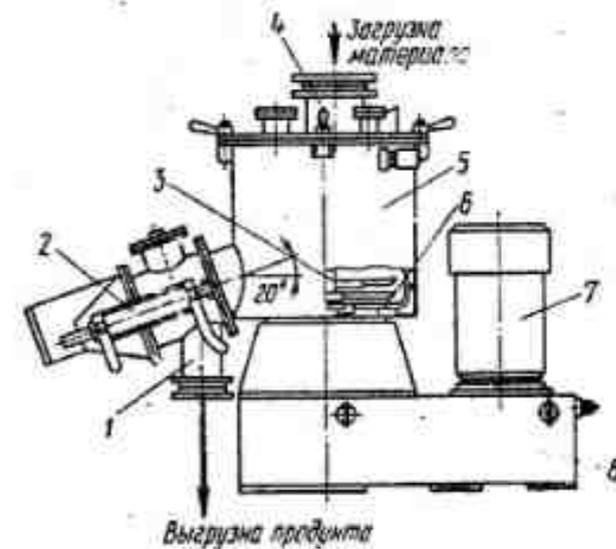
Смеситель центробежный лопастный типа ЦЛ
